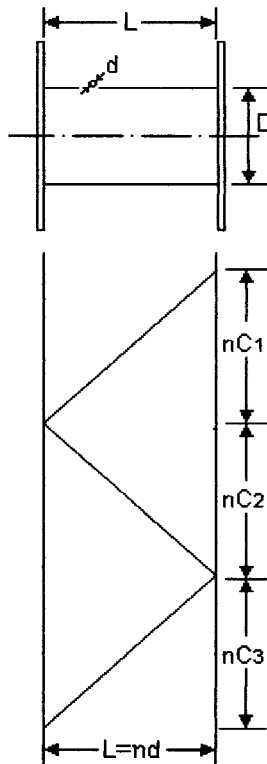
Desarrollo de Cable Enrollado en Tambor
